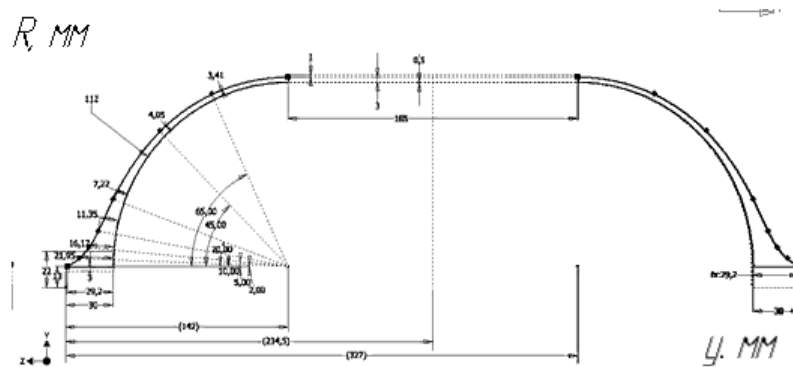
Расчётная геометрическая схема намотки малогабаритного корпуса с однослойной намоткой дна
